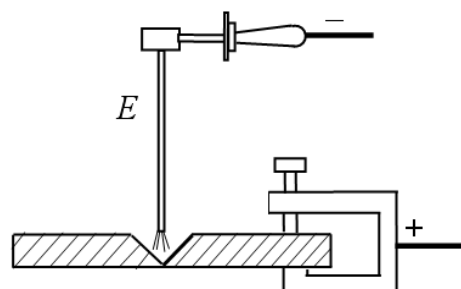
Soudage par le méthode de N. Slavyanov
